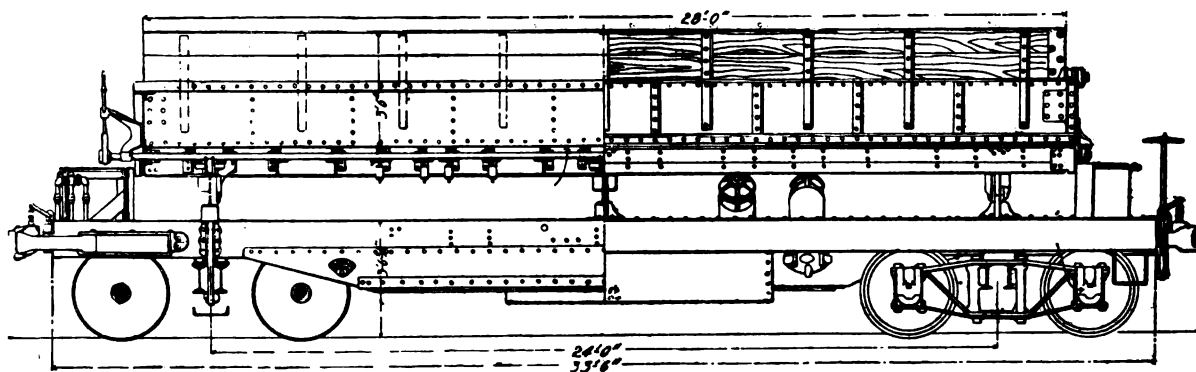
e 16. — Carro a scarico rapido. — Elevazione e sezione longitudinale.
